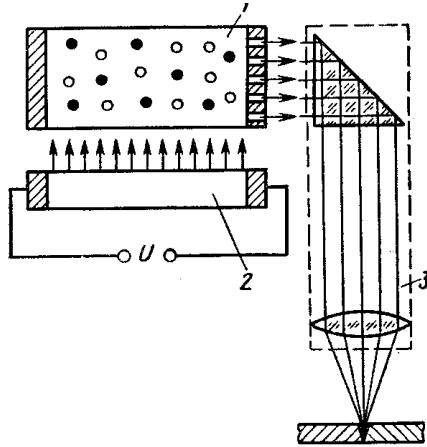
Схема установки для лазерной сварки с твердотельным лазером:
